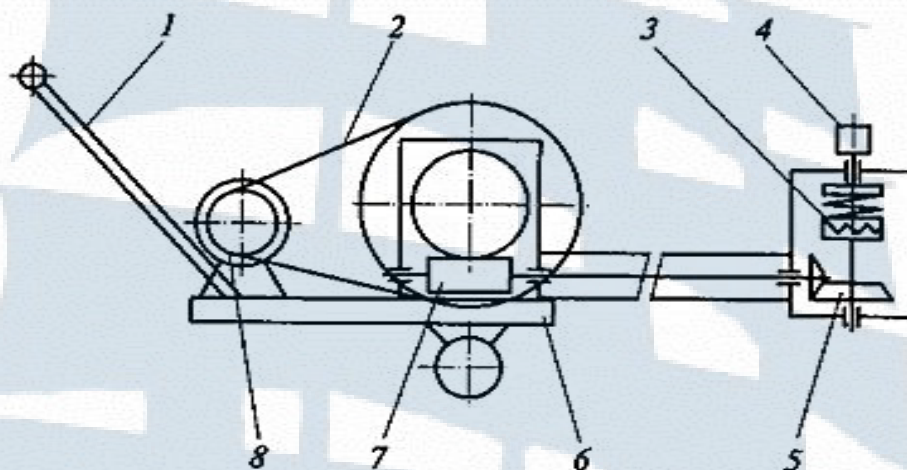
Схема гайковёрта для гаек стремянок рессор грузовых автомобилей:
